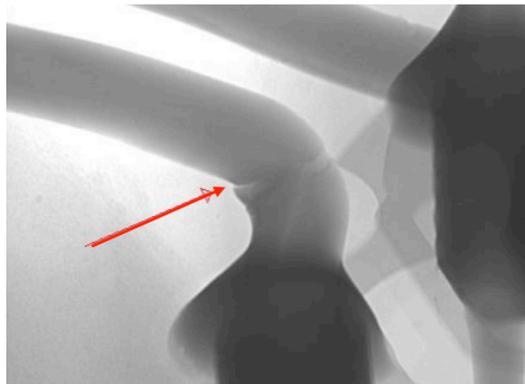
Acercamiento de la terminal del sensor magnético soldado a la tablilla electrónica, se observa una fractura en el doblado de la terminal.
